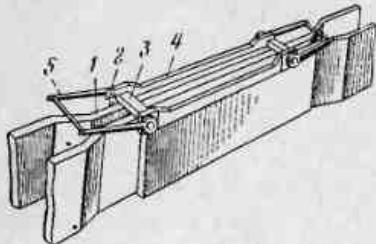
Кондуктор для пофазной сварки соединений секций ШМА.
